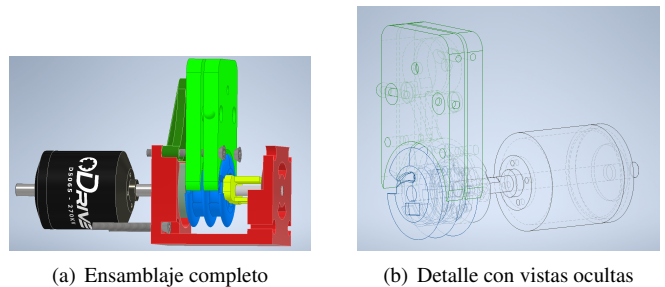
Vistas del sistema de mecánico de actuación para un motor. (a) Sistema completo. (b) Sistema de poleas y engranaje al eje del motor.
